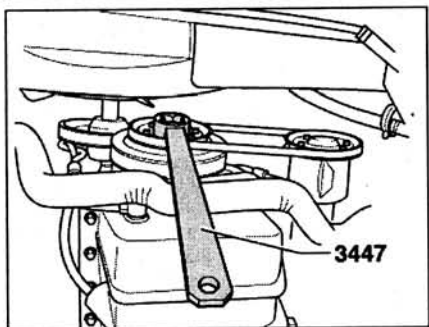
Прокрутите коленчатый вал с помощью ключа 3447.
